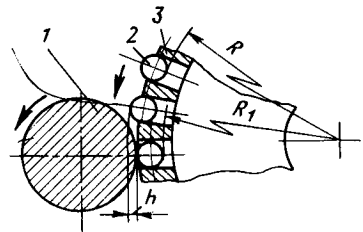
Схема процесса центробежной обработки поверхности шариками: 1 – обрабатываемая деталь; 2 – шарик; 3 – диск
